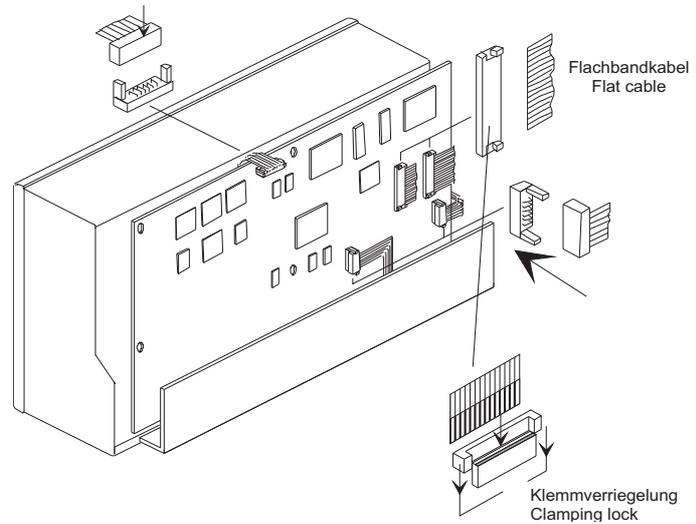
Anschlüsse an die locker eingesetzte Hauptplatine
